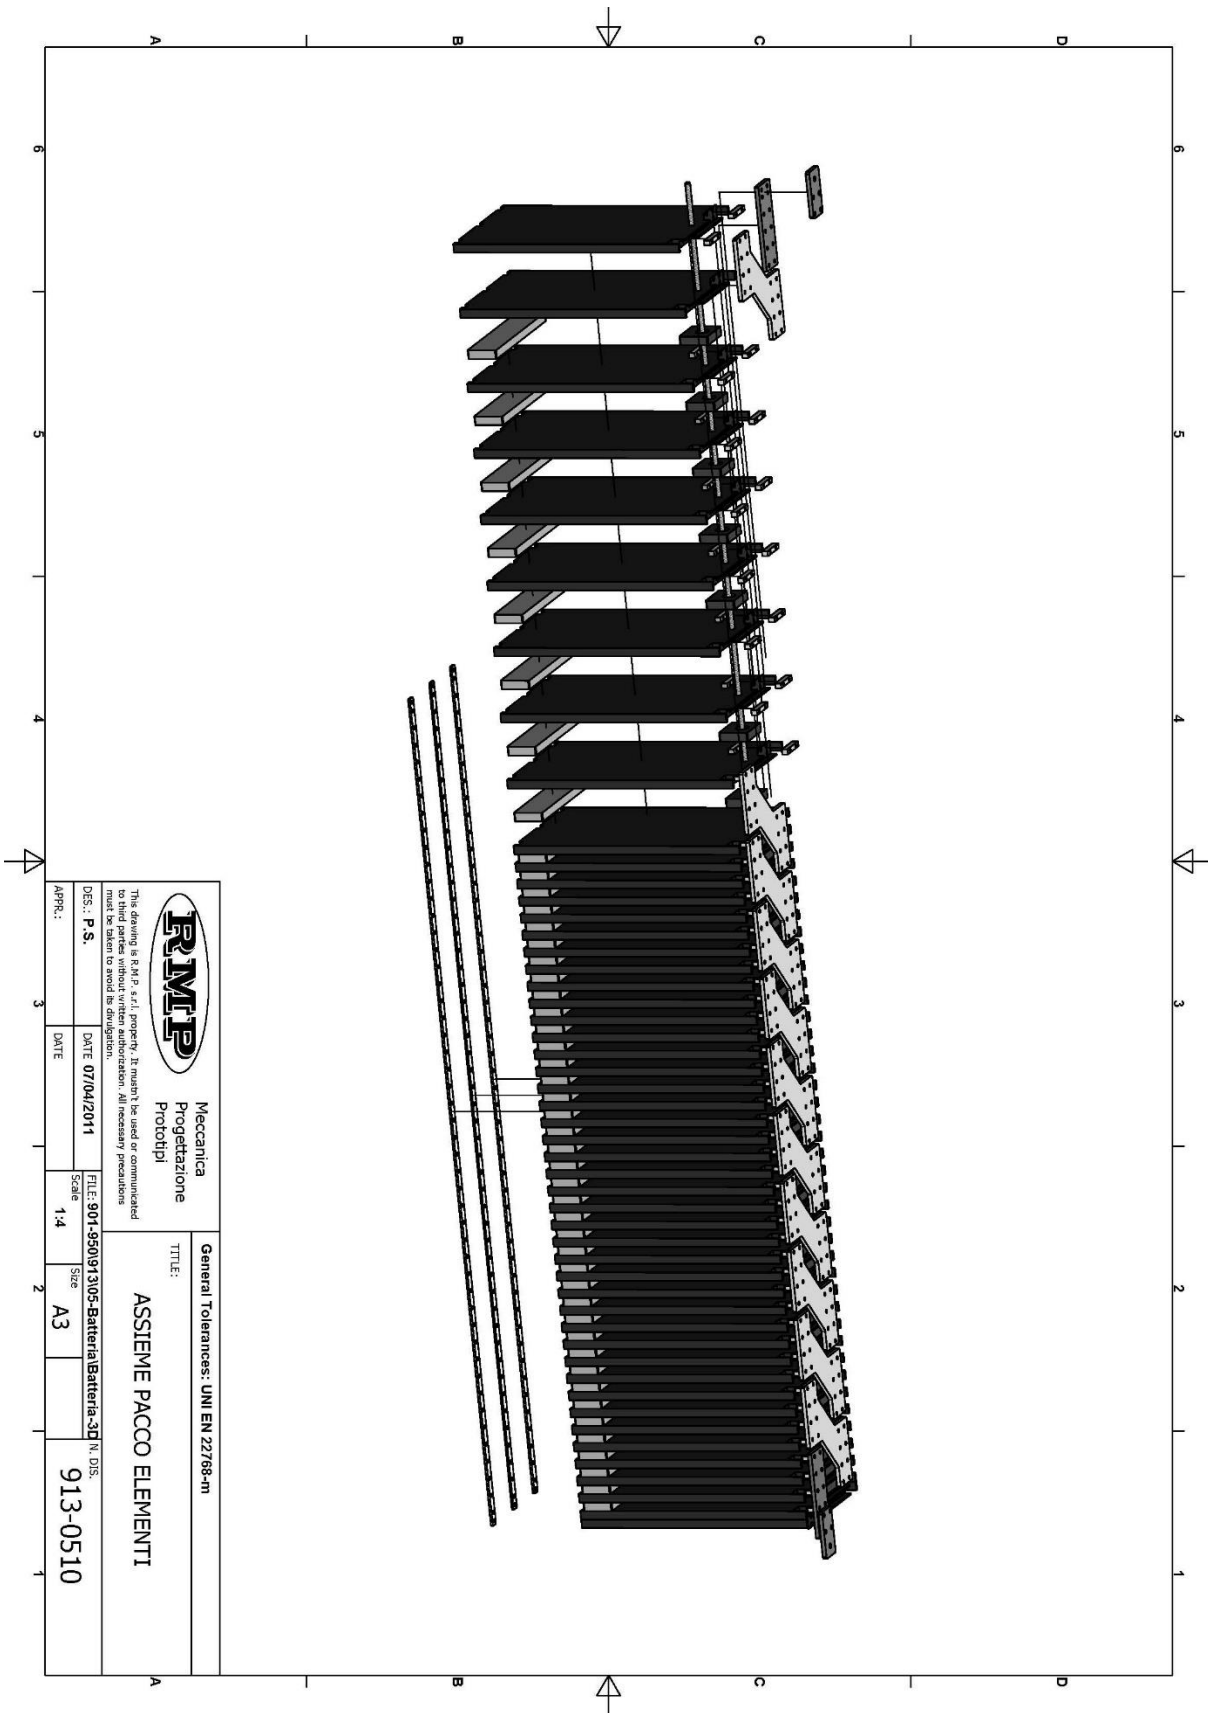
Disegni di assemblaggio del modulo di Bergamo – parte interna
